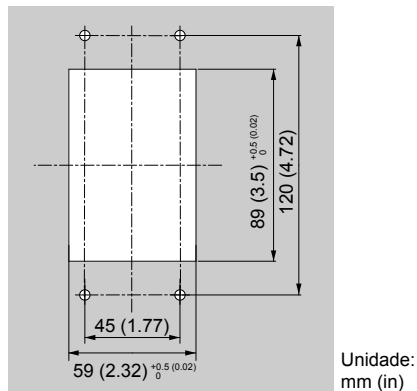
Dimensões de corte do painel (instalação de montagem interna/embutida)
